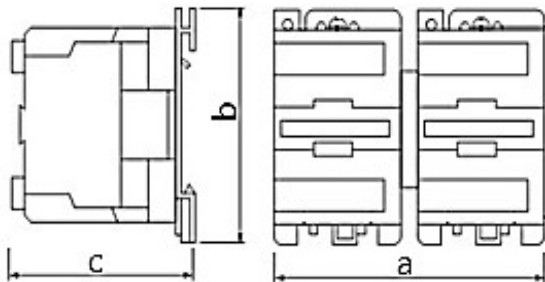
Пускатели реверсивные габаритов 063 без оболочек
